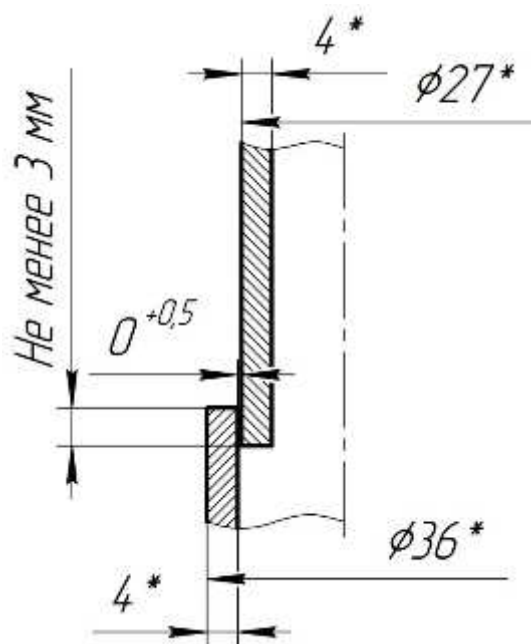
Геометрические размеры собираемых кромок при сварке муфт с трубками и патрубками
